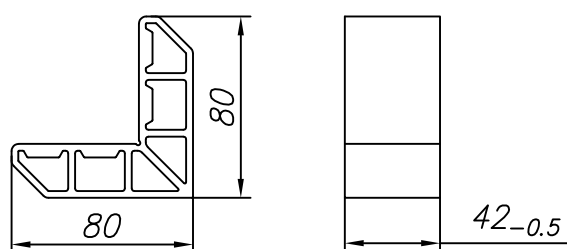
Изготовление соединителя углового FLGU.400.0914
